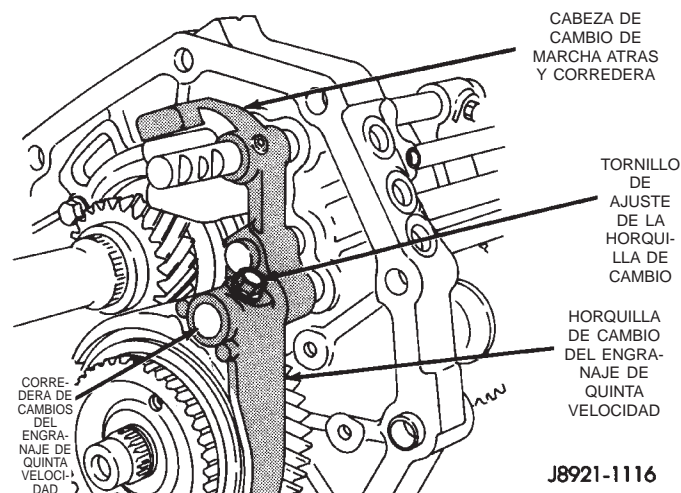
Instalación de perno de retén de horquilla de cambio de engranaje de quinta velocidad
